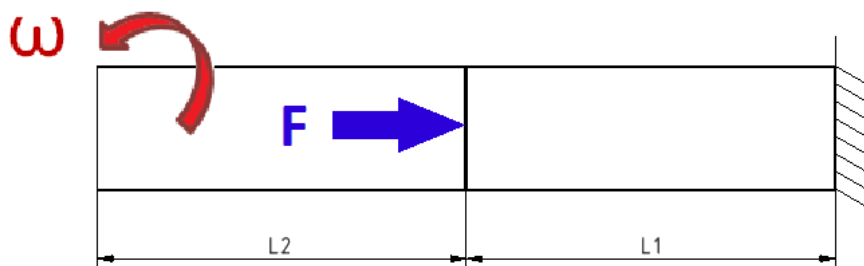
Representación esquemática del proceso de soldadura por fricción rotativa. [Autor]
